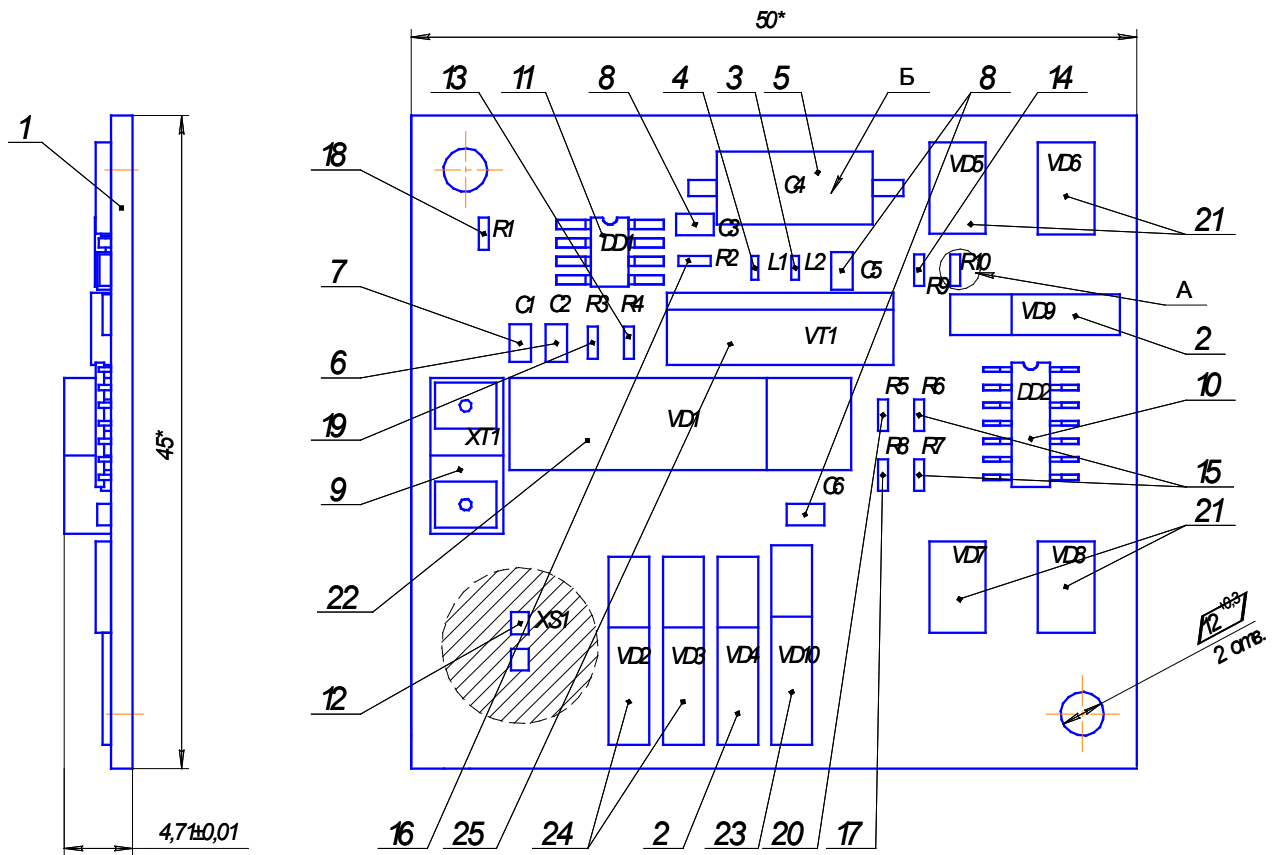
Пример сборочного чертежа платы печатной с элементами поверхностного монтажа
